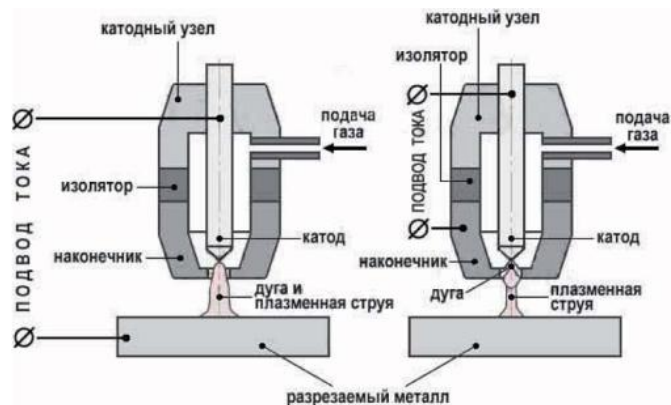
Схема режущего плазмотрона: а) Схема плазменно-дуговой резки; б) схема резки плазменной струей
